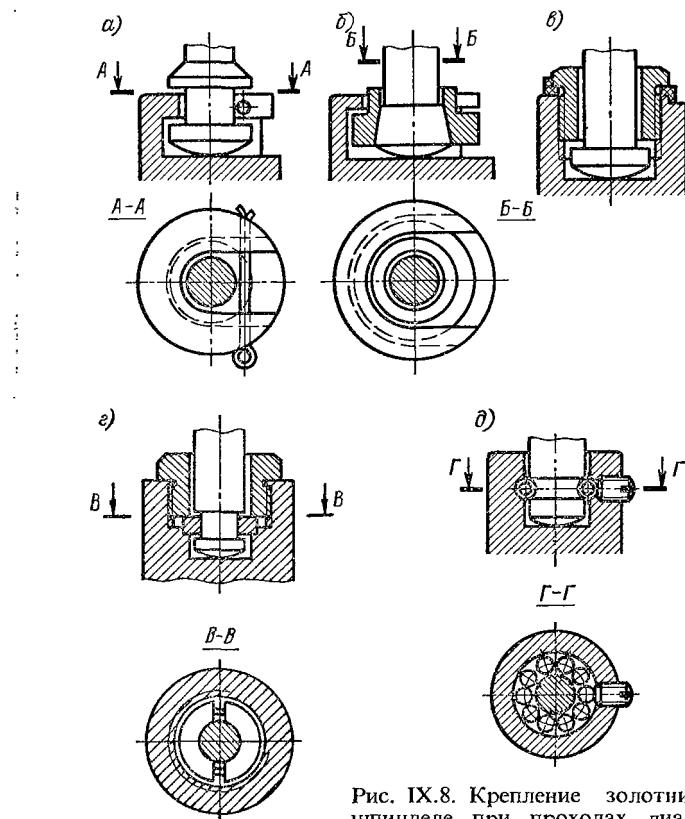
Крепление золотника на шпинделе при проходах диаметром выше 55 мм: *а* – с помощью шплинта; *б* – с помощью кольца; *в* – резьбовой втулкой; *д* – резьбовой втулкой со стопорной шайбой; *д* – шариками со стопорным винтом (рекомендуется для арматуры, работающей при повышенной температуре – до 300°C)
